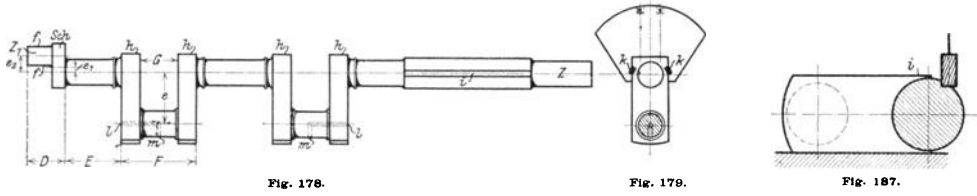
u. 179. Kurbelwelle für 2-Zylinder-Dieselmotor.
